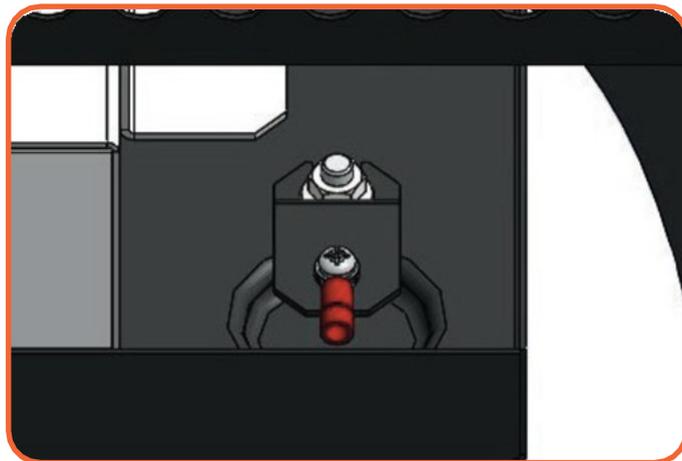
Sensore di rilevamento perdite nel punto più basso
